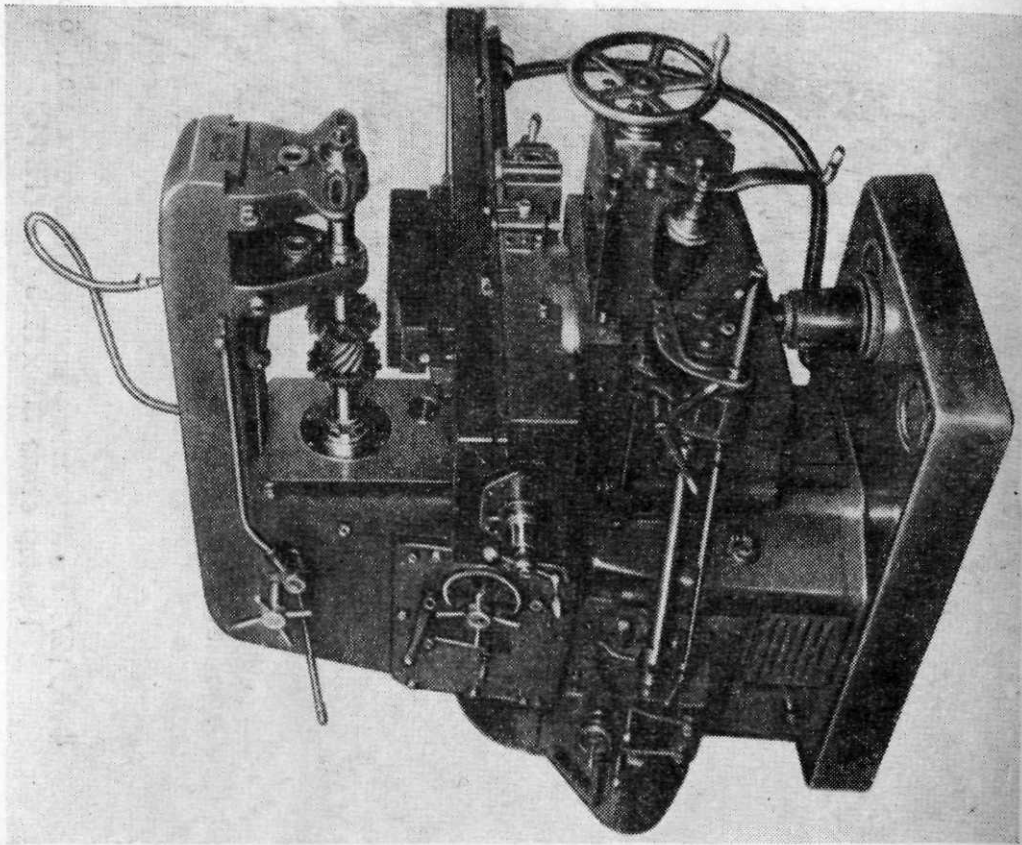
Универсально-фрезерный станок мод. 6B82.
